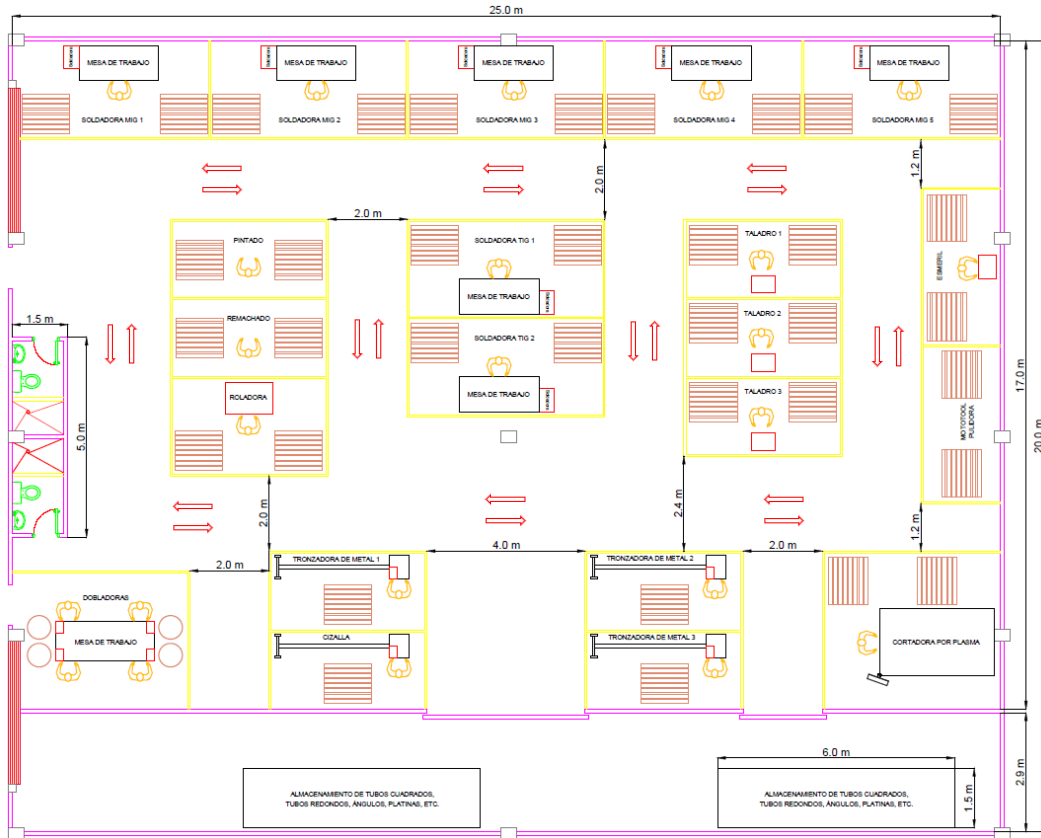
Opción 1 de Layout realizado en AutoCAD de 425 m². Fuente: Autor.
